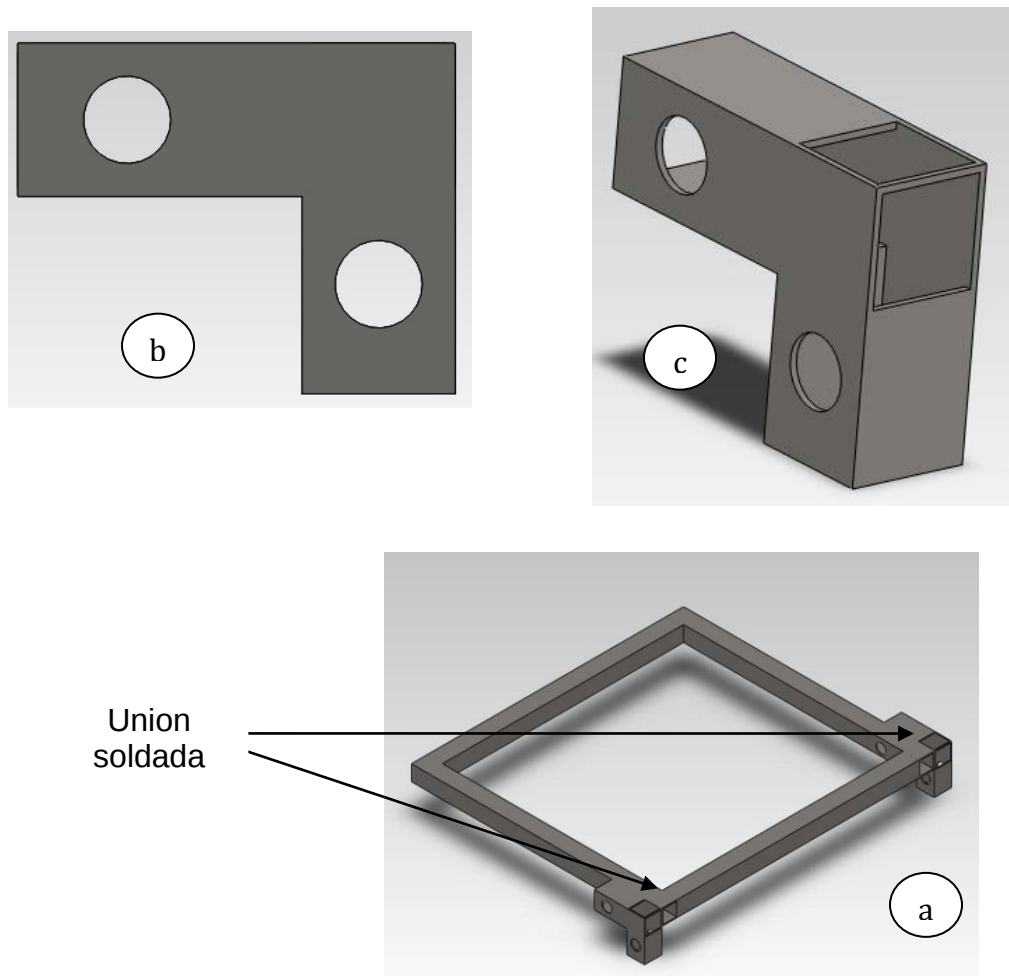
Espaldar del rehabilitador de rodilla (a) Vista isométrica del espaldar, (b) Vista frontal unión del chasis espaldar, (c) Vista isométrica unión del chasis espaldar
